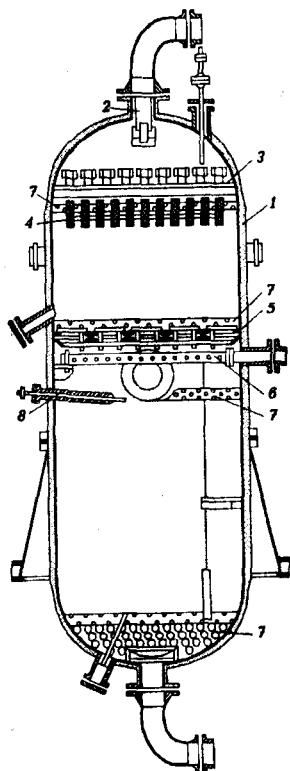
Реактор гидроочистки дизельного топлива: 1 – корпус; 2 – распределитель и гаситель потока; 3 – распределительная непровальная тарелка; 4 – фильтрующее устройство; 5 – опорная колосниковая решетка; 6 – коллектор ввода водорода; 7 – фарфоровые шары; 8 – термопара
